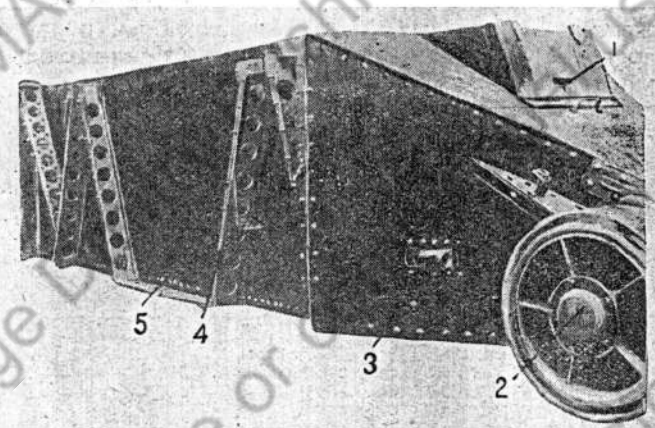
Общий вид передней части корпуса со снятой бортовой броней.
